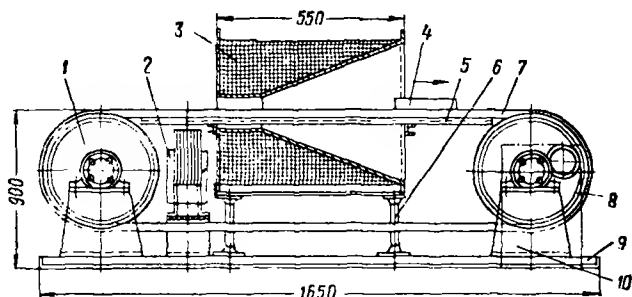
Устройство для размагничивания деталей роликовых подшипников:
